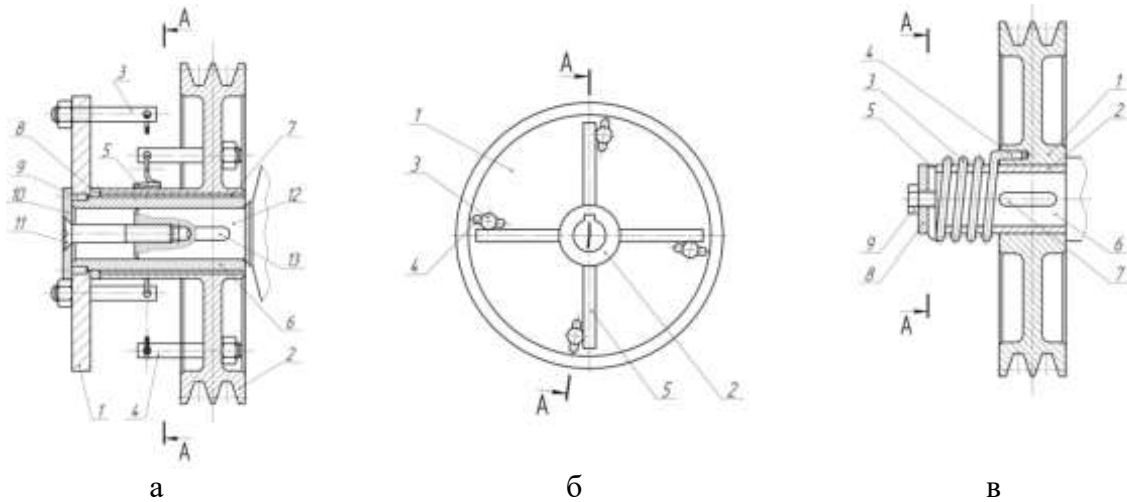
Нові конструкції пружних муфт: а – з циліндричними пружинами розтягу; б – з консольними плоскими пластинчастими пружинами; в – з циліндричною пружиною кручення
